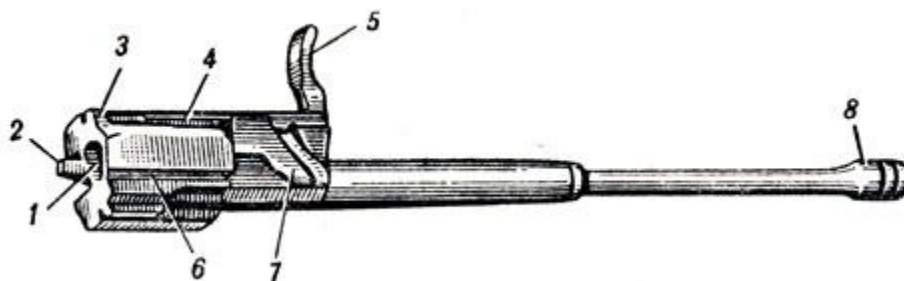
Затворная рама с газовым поршнем: 1 - канал для затвора; 2 - предохранительный выступ; 3 - выступ для опускания рычага автоспуска; 4 - паз для отгиба ствольной коробки; 5 - рукоятка; 6 - паз для отражательного выступа; 7 - фигурный вырез; 8 - газовый поршень
